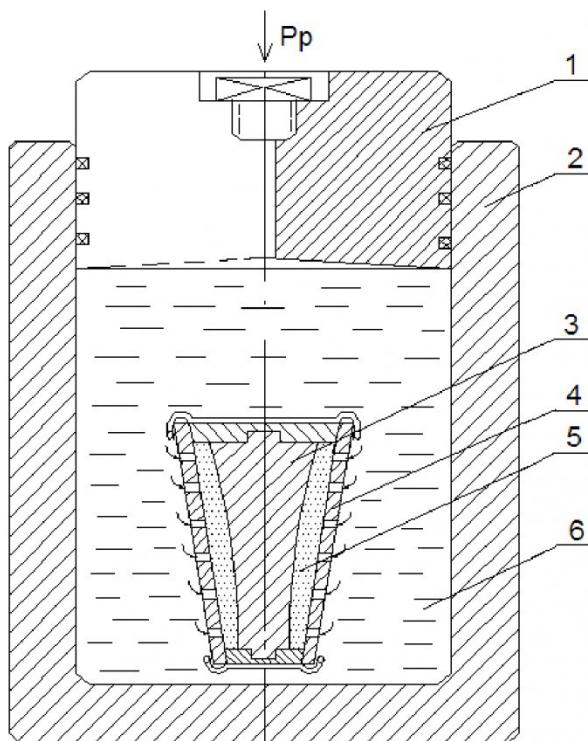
Схема гидростатического прессования: 1 - плунжер, 2 - технологическая ёмкость, 3 - пuhanсон-стержень, 4 - пресс-форма, 5 - смесь - заготовка, 6 - глицерин (или масло).
